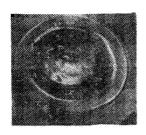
Внешний вид соединения, выполненного дуговой точечной сваркой с
